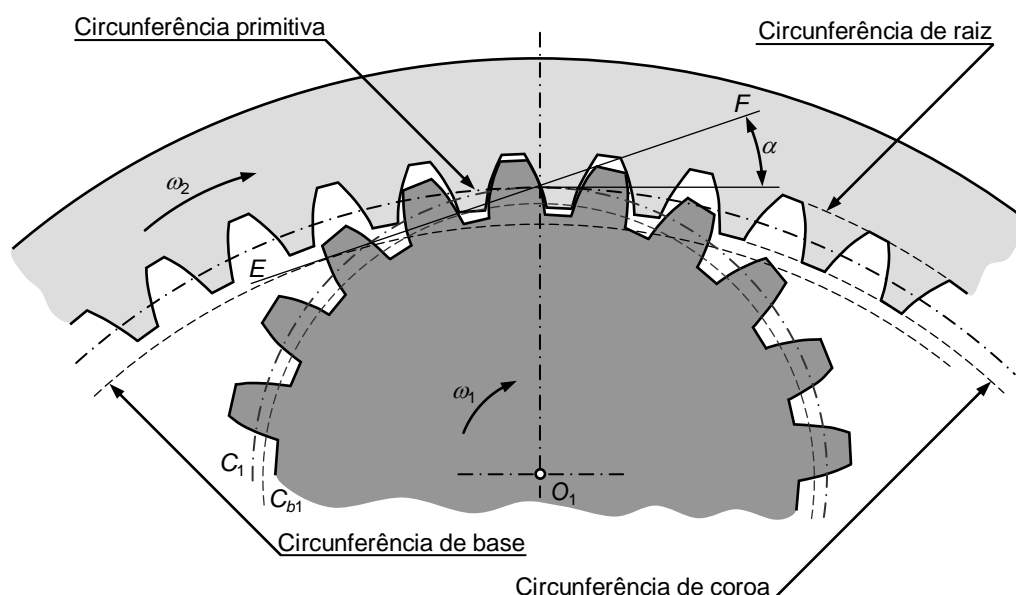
Engrenagem cilíndrica interior de dentes retos.
